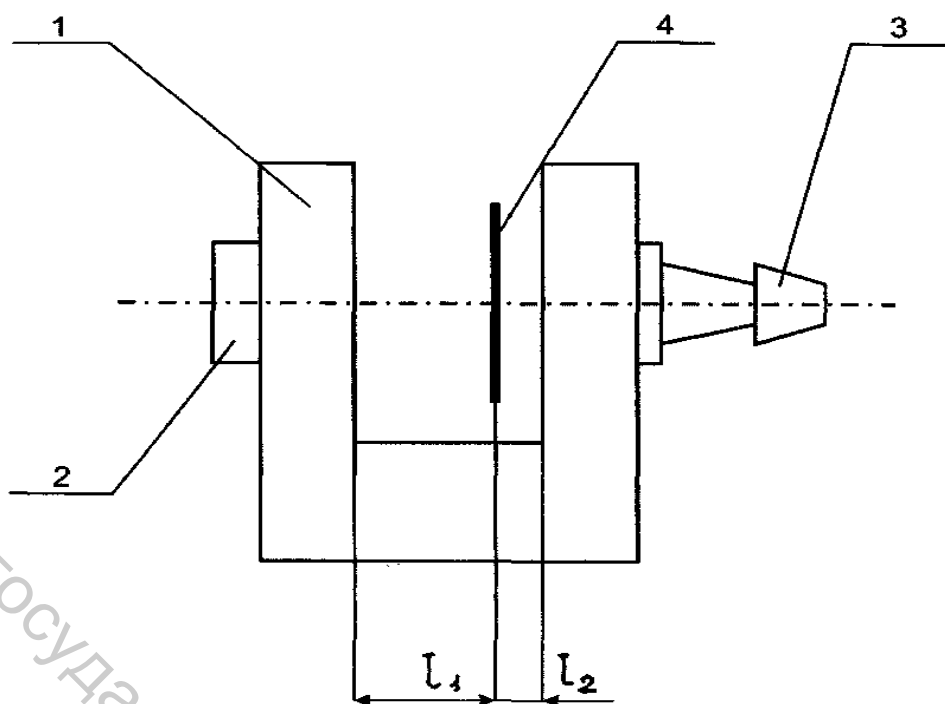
Конструктивная схема структурного путевого переключателя: 1 – корпус; 2 – входной штуцер; 3 – выходной штуцер; 4 – лепесток
